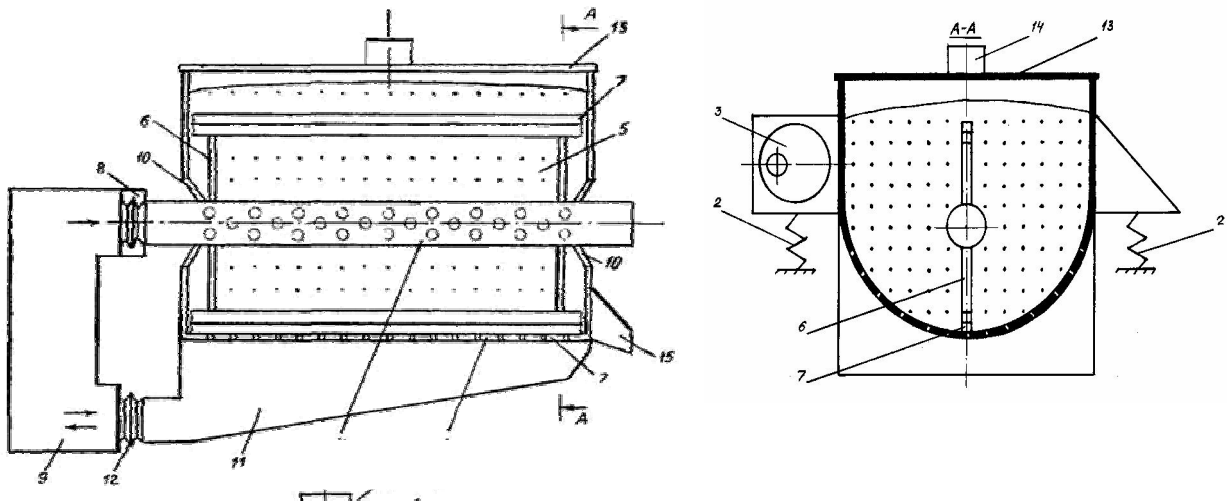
Конструктивна схема вібраційної сушарки для фільтраційно-конвективного сушіння насіння гарбуза: 1-робоча камера; 2-пружины; 3-віброзбудувач дебалансний; 4-пустотілий циліндр; 5-насіння; 6-лопати; 7-скребки; 8, 12-з'єднання еластичне; 9-агент сушильний; 10-пружні вставки; 11-дифузор; 13-панель верхня; 14-отвір завантажувальний; 15-лоток розвантажувальний.
